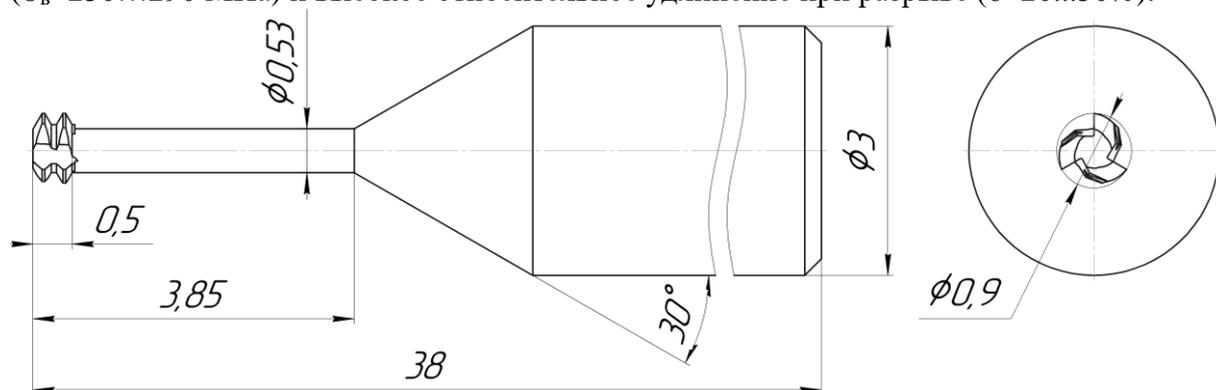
Резьбовая фреза для обработки резьбы М1,2х0,25.
